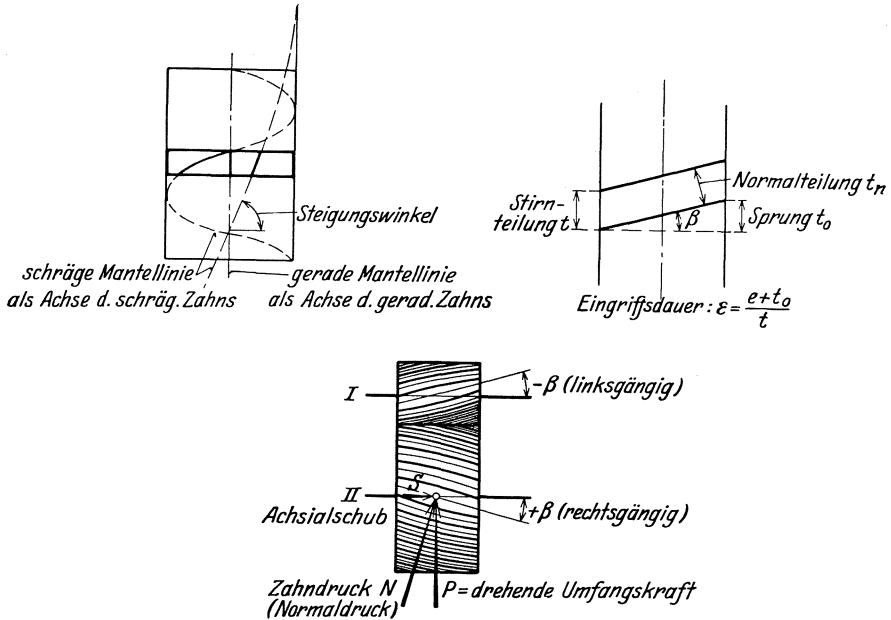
bis 254. Stirnräder mit schrägen Zähnen.
